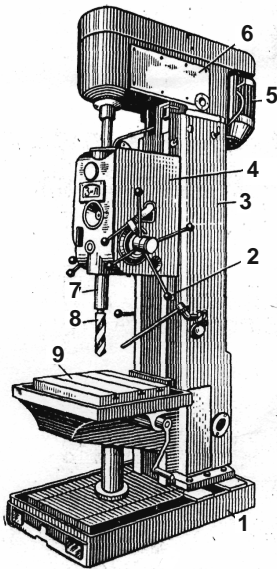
Вертикально-свердлильний верстат:
